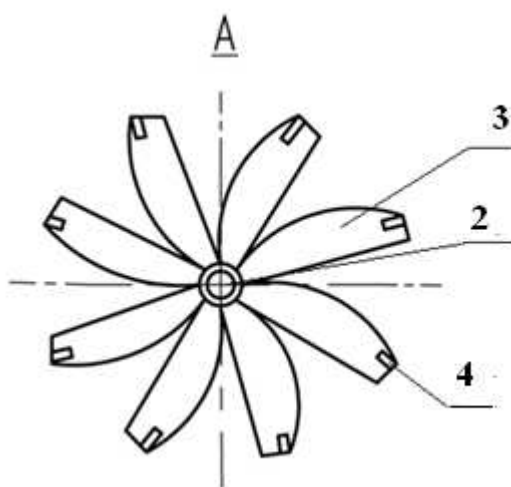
Вид А сверху на лопатки с пластинчатым упором
